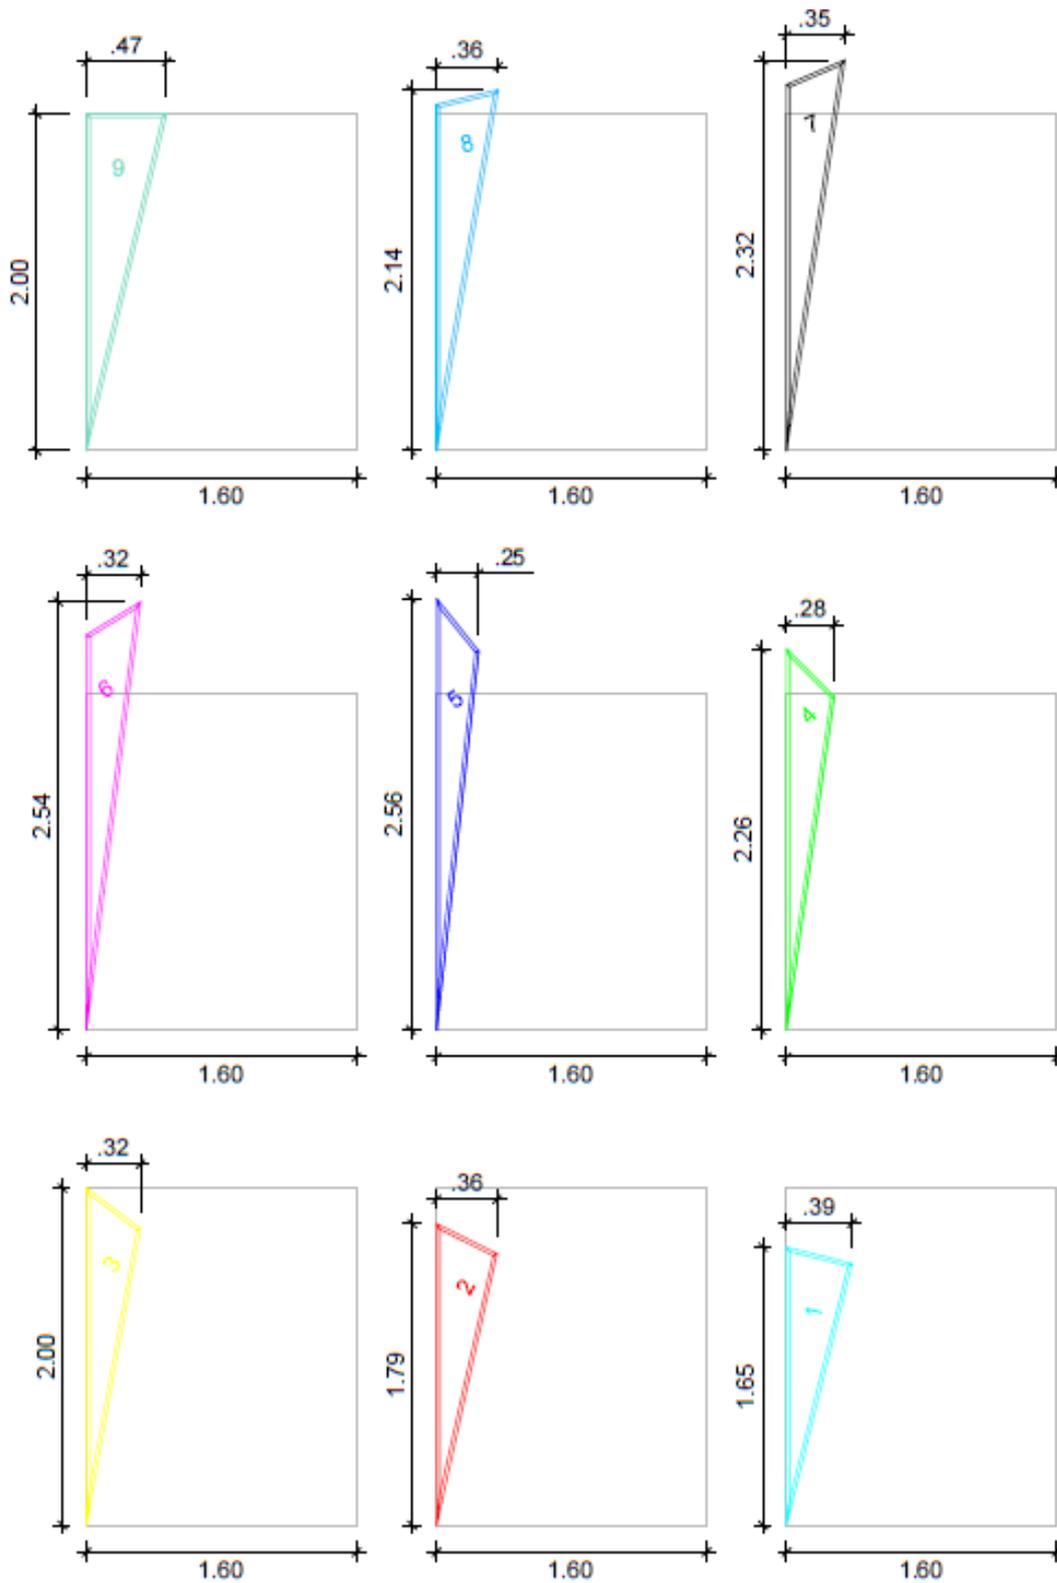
Vista frontal de la puerta en abanico en posición cerrada con sus dimensiones.
